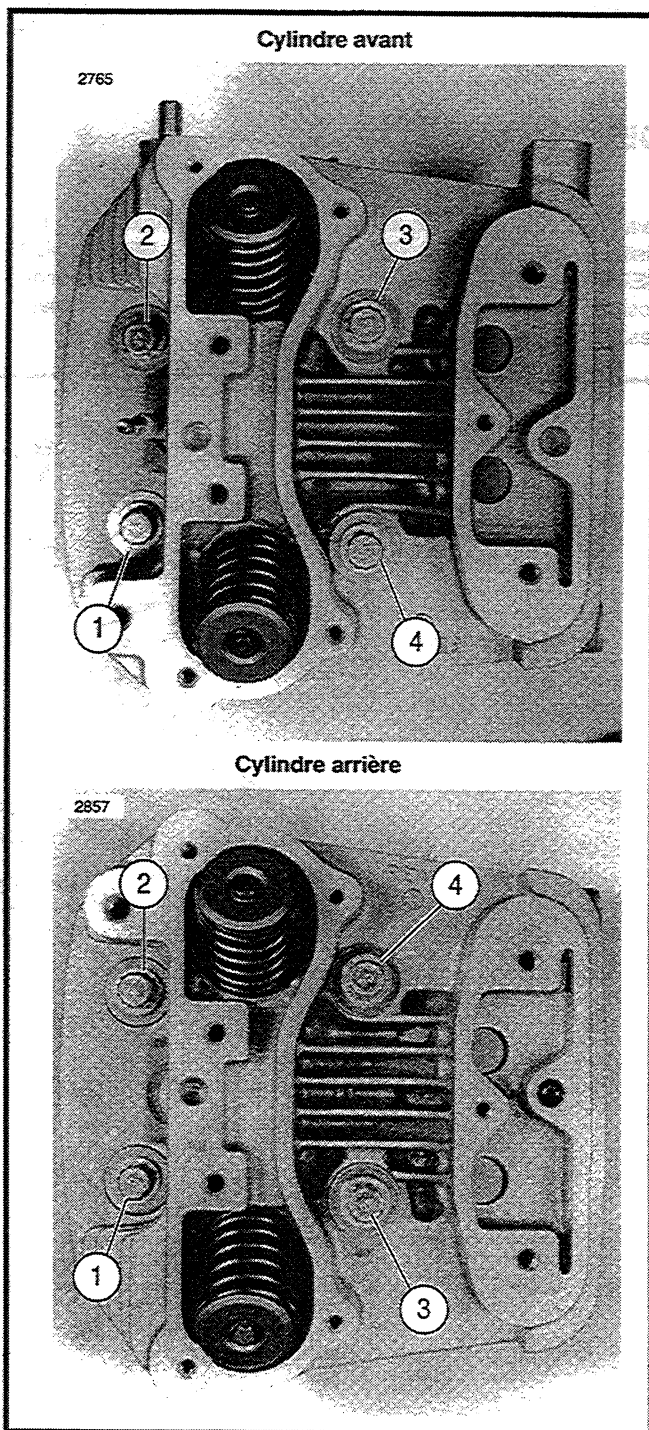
Séquence de serrage/desserrage des vis de culasse
